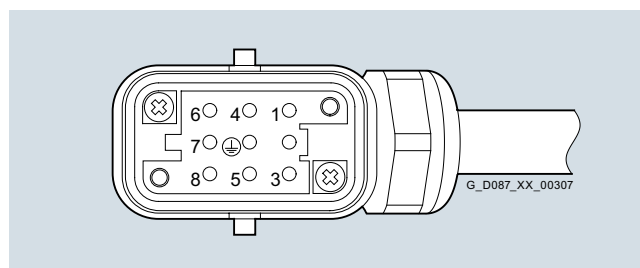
/29 Pinbelegung bei Motorstecker mit Kabel 1m bis 5m
